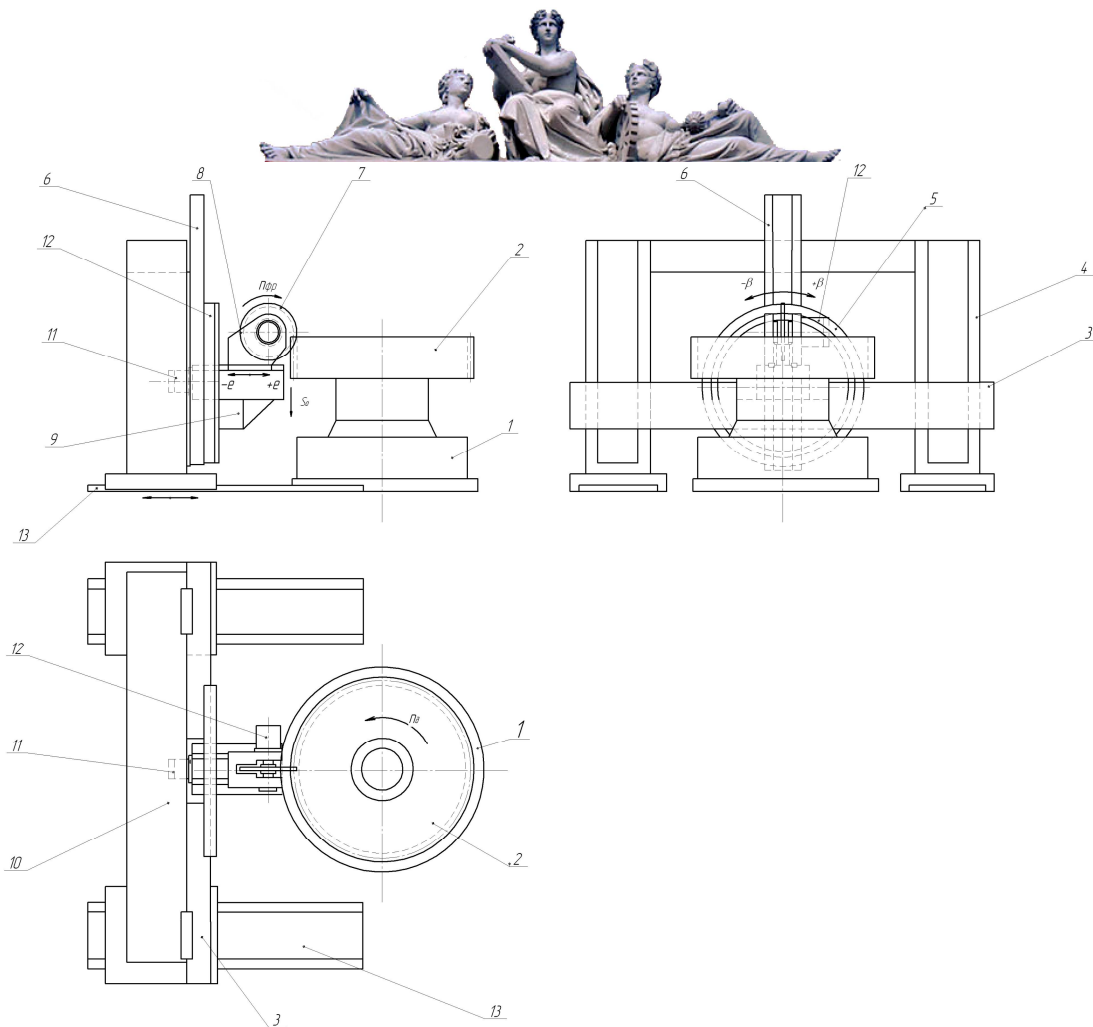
Будова зубофрезерного верстата на основі радіально-колового способу зубонарізання на базі компоновки важкого токарно-карусельного верстата
